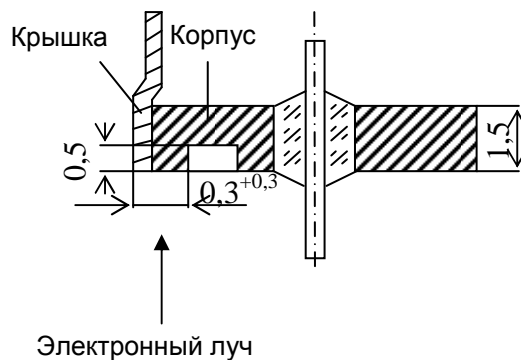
Форма кромок металлоглазненного корпуса под электронно-лучевую сварку
